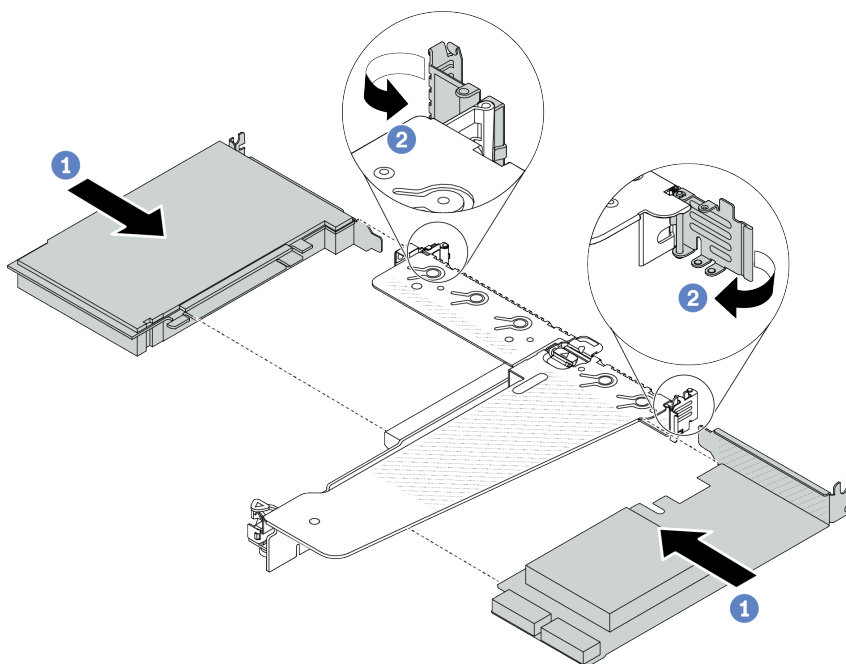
Instalação do adaptador PCIe no conjunto de placa riser LP-FH
